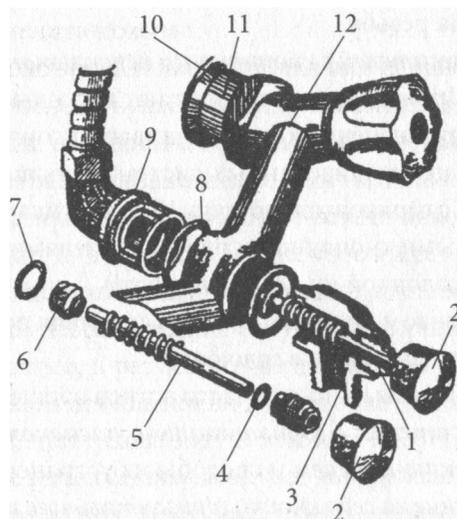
Смеситель с горизонтально расположенным кнопочным переключателем: 1 — специальный винт; 2 — кнопка; 3 — переходник; 4 — резиновое кольцо сальника; 5 — шток; 6 — клапан; 7 — резиновое кольцо клапана; 8 — резиновая прокладка; 9 — крышка; 10 — декоративная шайба; 11 — патрубок; 12 — корпус
